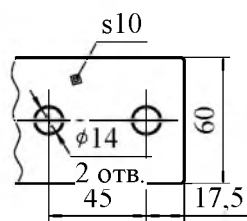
Разметка отверстий для присоединения ошиновки
